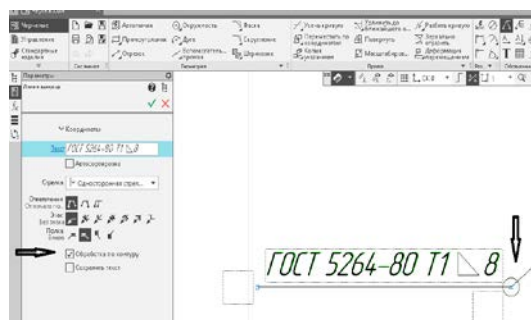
Указание на условном обозначении сварного шва выполнения сварного шва по замкнутой линии.
